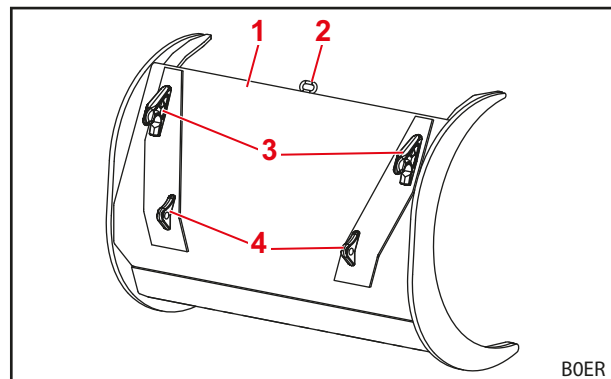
Конструкция ковшовых вилок для бревен Н – вид сзади
